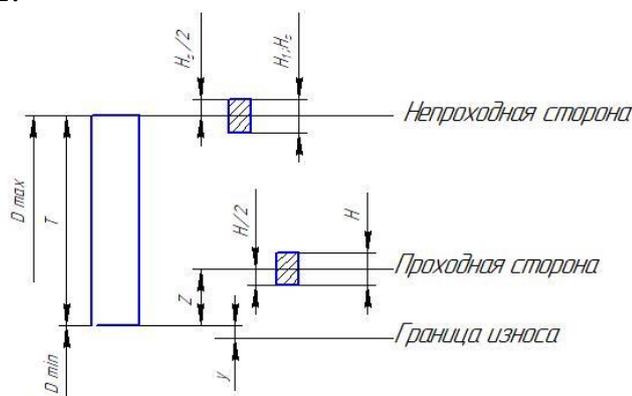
Схема расположения полей допусков калибров для контроля отверстий.
